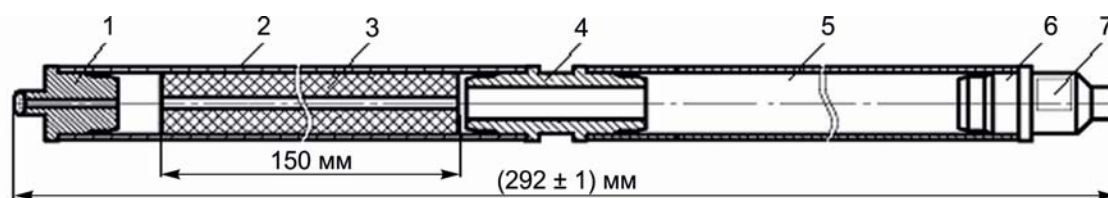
Схема рефабрикованного твэла: 1 — концевик; 2 — фрагмент полномасштабного твэла; 3 — топливный сердечник; 4 — переходник; 5 — компенсационный объём; 6 — верхняя заглушка; 7 — место нанесения маркировки твэла
